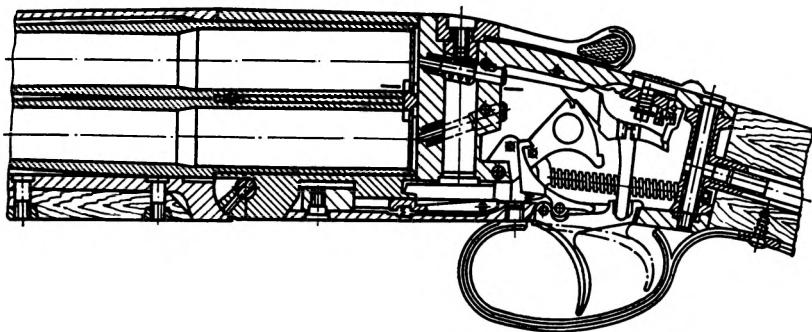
Схема устройства ударно-спускового и предохранительного механизмов ружья ИЖ-15
